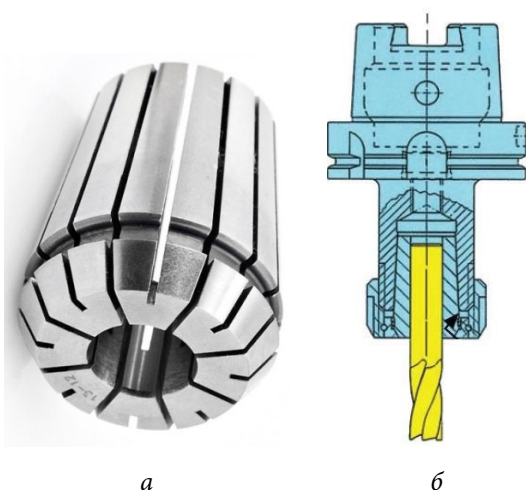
Цанга: а — внешний вид; б — схема патрона
